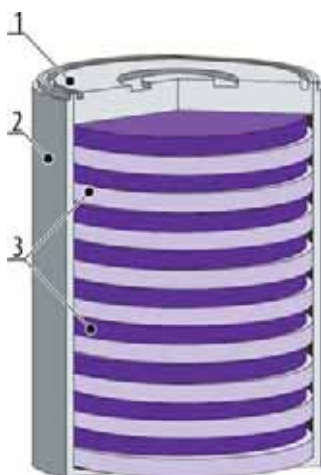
Конструкция макета источника: 1 — крышка; 2 — корпус; 3 — имитаторы активной части
